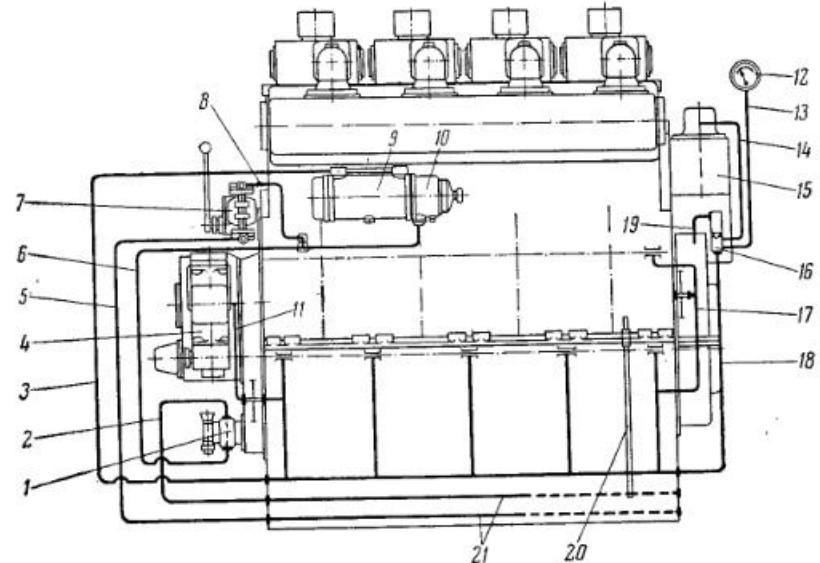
Схема системы смазки двигателей типа NVD-24:
